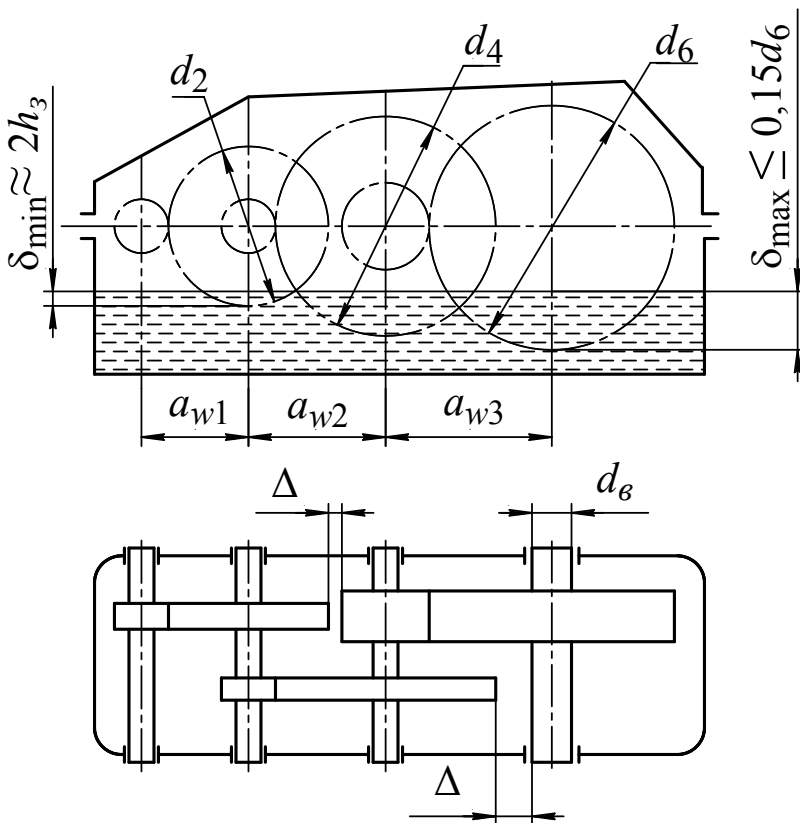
Сборочная компоновка редуктора (выполняется в масштабе)
